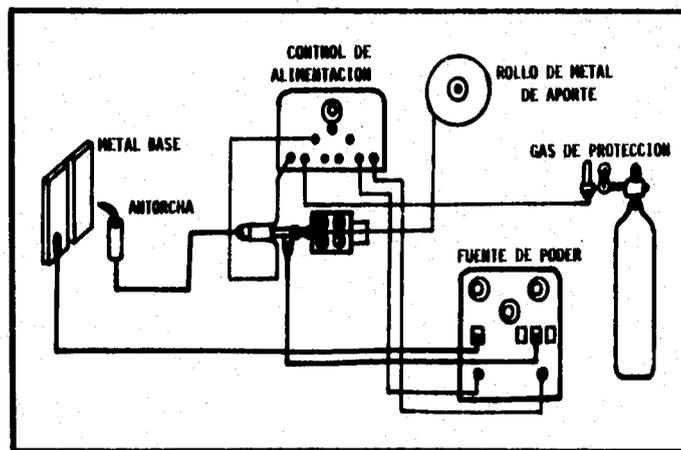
DETALLE DEL PROCESO DE SOLDADURA GMAW.
